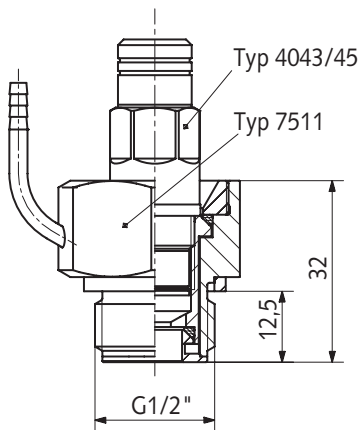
Einbau des Sensor Typs 4045A... in gedämpften Kühladapter Typ 7511
